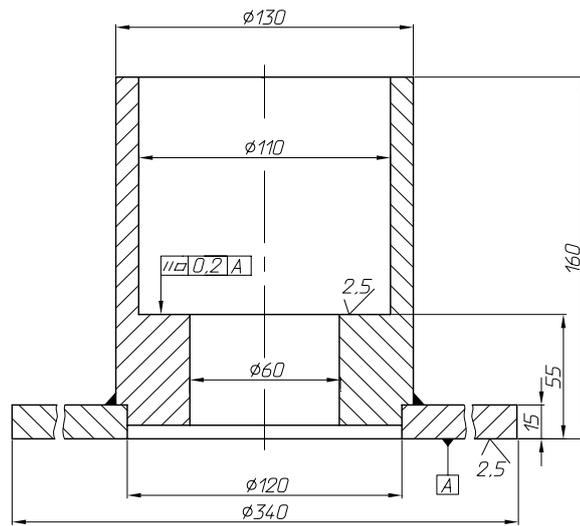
Конструкция подставки и последовательность спресовки шестерён вала промежуточного КП типа ЯМЗ-239
